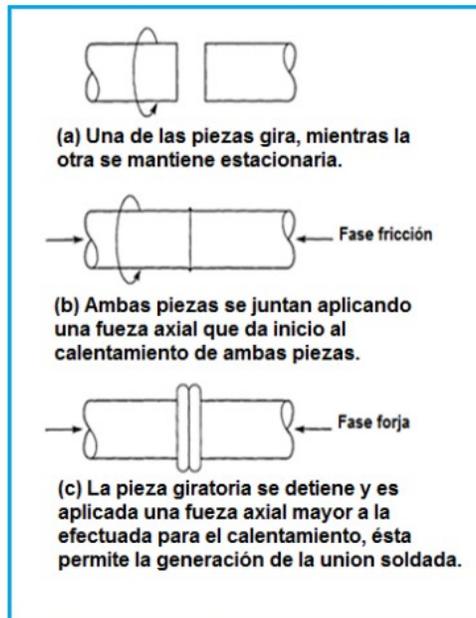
Etapas fundamentales de la soldadura por fricción rotativa.
